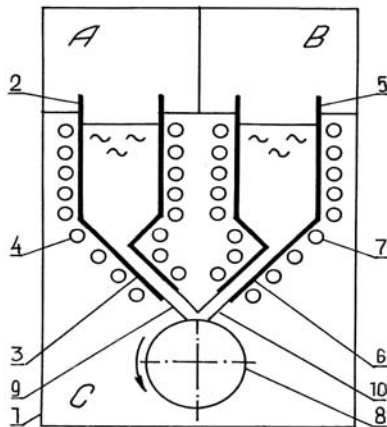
Схема устройства для быстрой закалки сплава со сливом расплава тонкой струёй на быстро вращающийся кристаллизатор: 1 – камера, разделённая на секции А, В и С; 2 и 5 – тигли; 4 и 7 – нагреватели; 3 и 6 – сопла; 8 – кристаллизатор; 9 и 10 – струи
